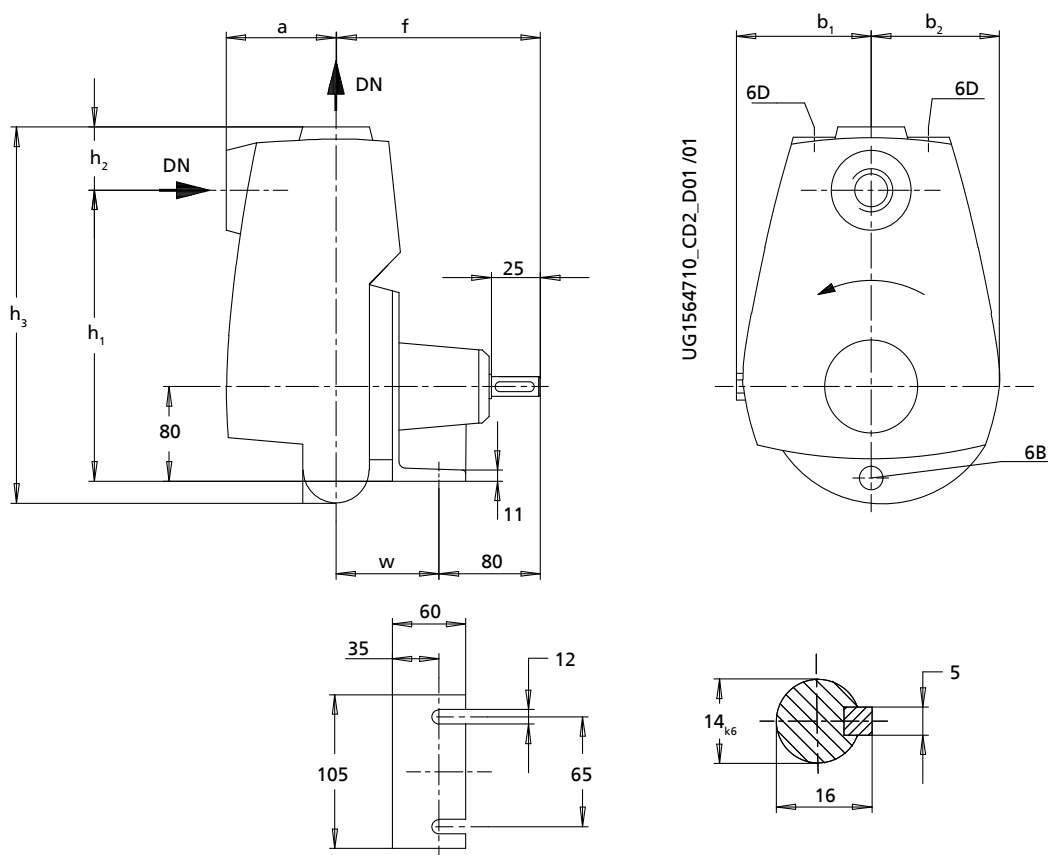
Габаритные размеры типоразмер с 025-025-100 по 040-040-110 (узел вала 17) — насос
